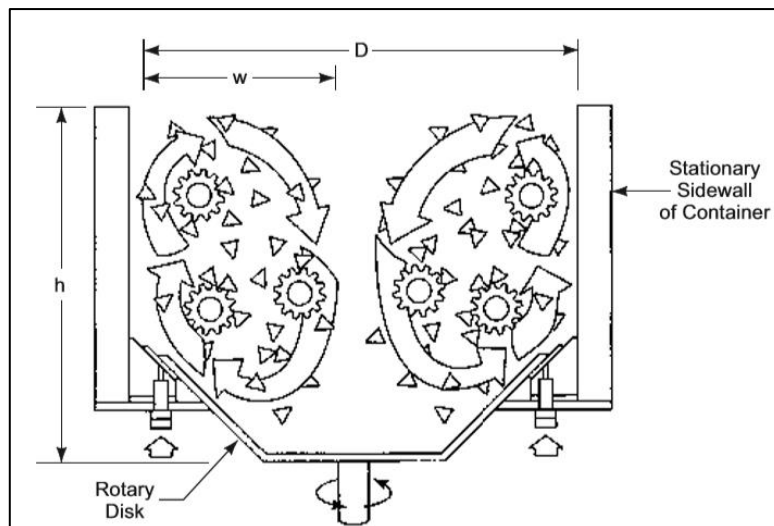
Principe de la machine centrifugeuse à fond tournant [1]
